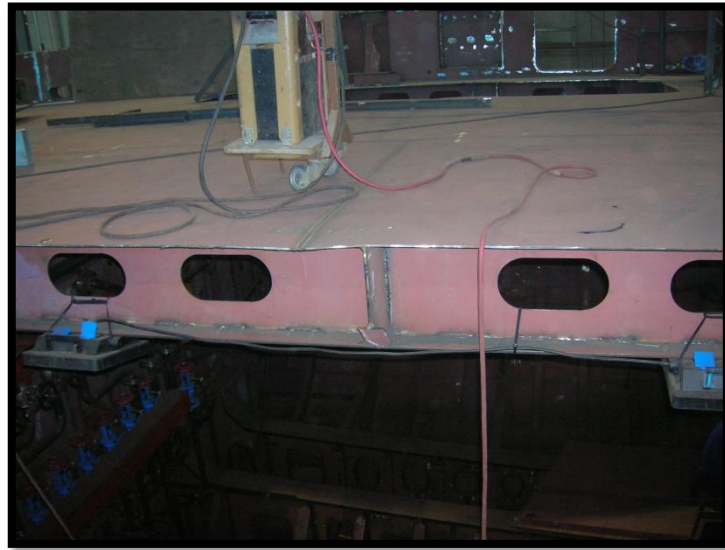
Detalle aligeramiento en cubierta del buque
